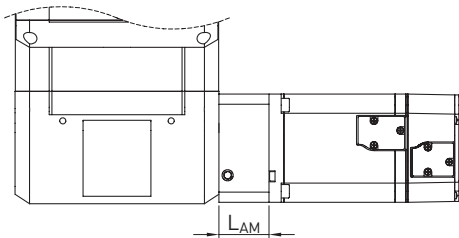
Motoranbindung Lineartisch HT-B ohne Getriebe
